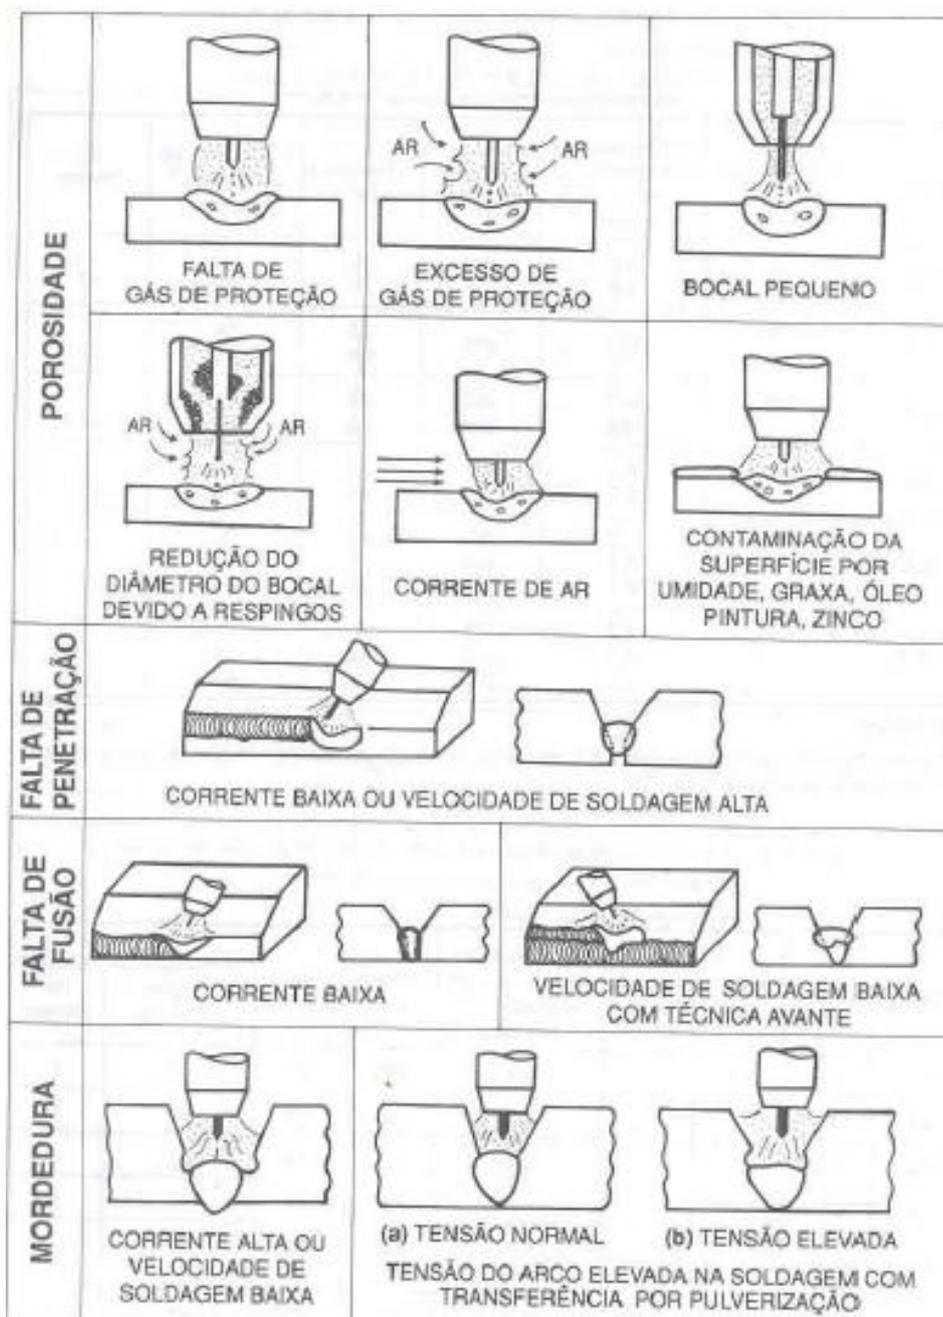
Possíveis problemas na soldagem MIG/MAG
